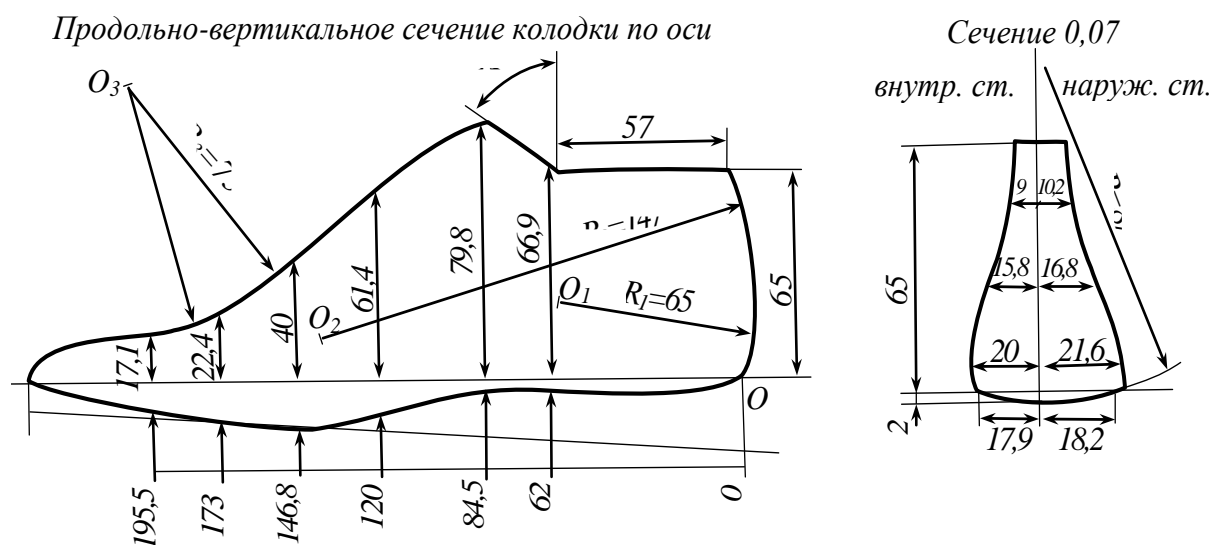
Колодка для девичьей закрытой обуви
